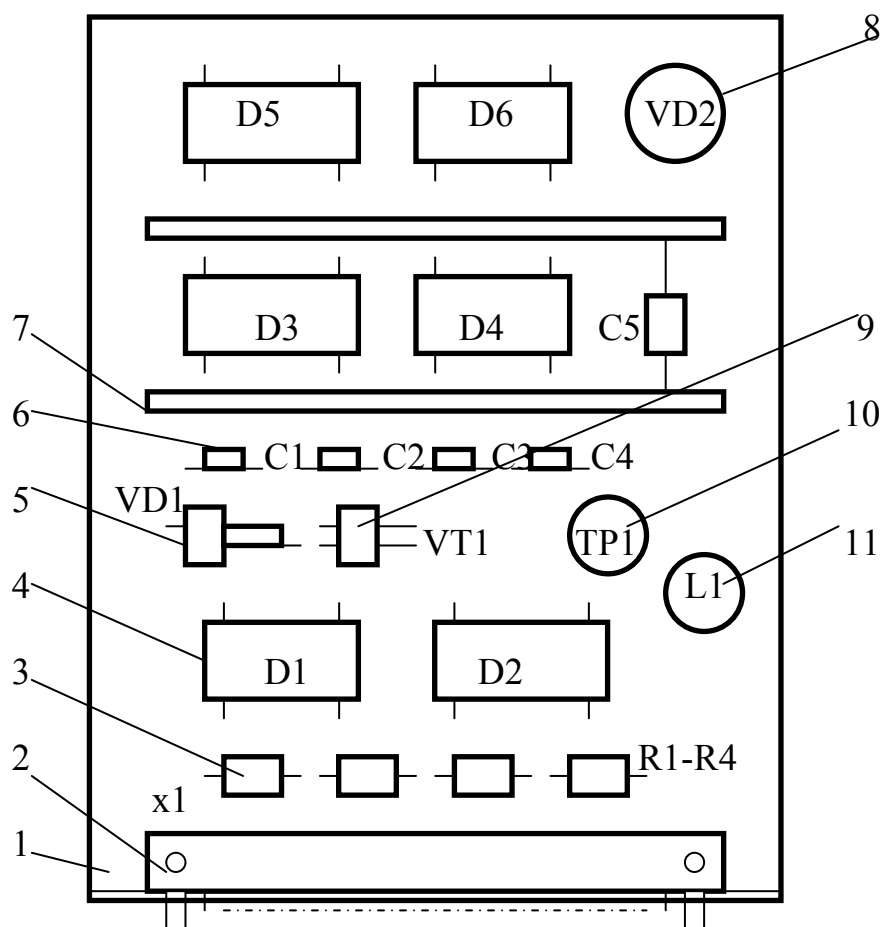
Сборочный чертеж печатного узла в 2D виде
